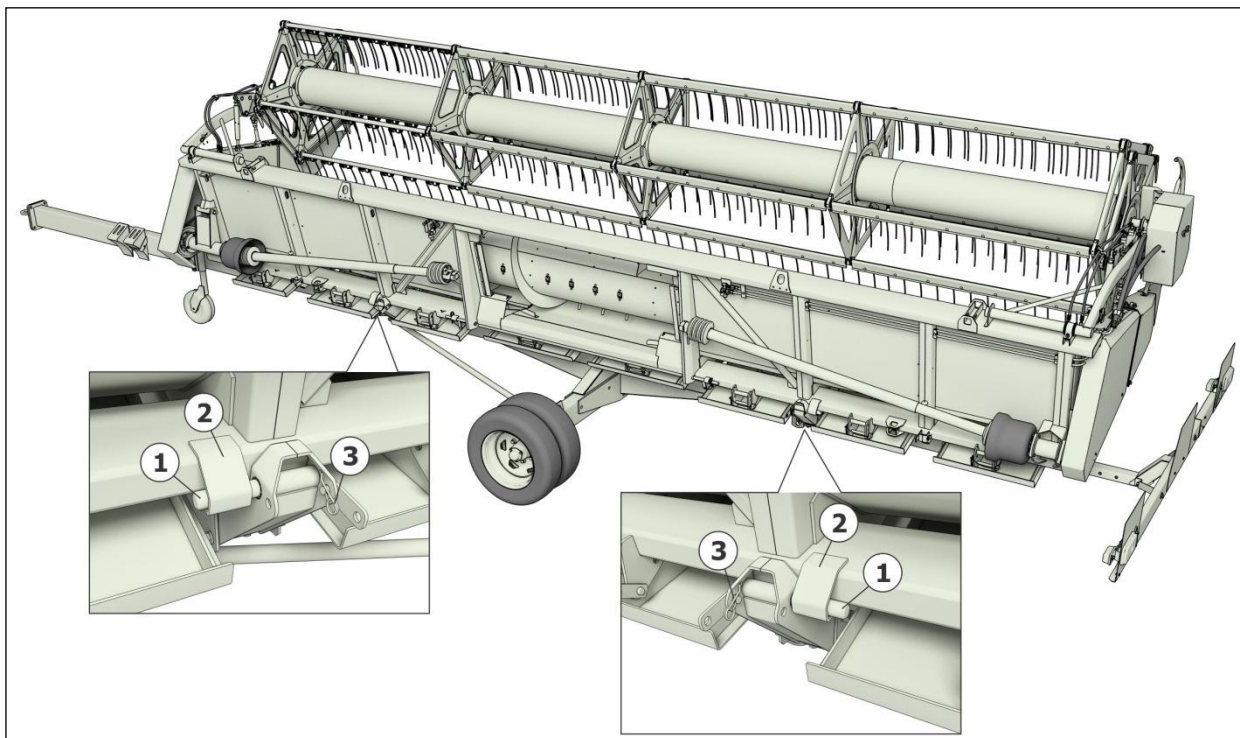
Подготовка тележки РСМ-142.29 для установки жатки
